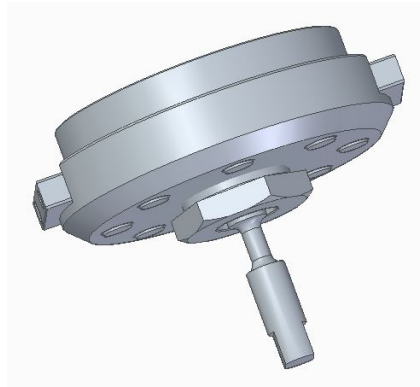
Afferraggio realizzato dall'Università di Roma.
